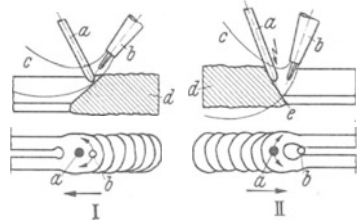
Draht- und Brennerführung sowie Schuppenkette (I Nachlinksschweißung, II Nachrechtsschweißung).
